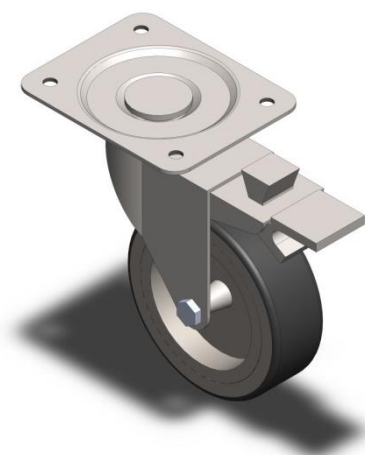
Arxiu CAD de les rodes model A-PU 2-1216 (TraceParts S.A.,
